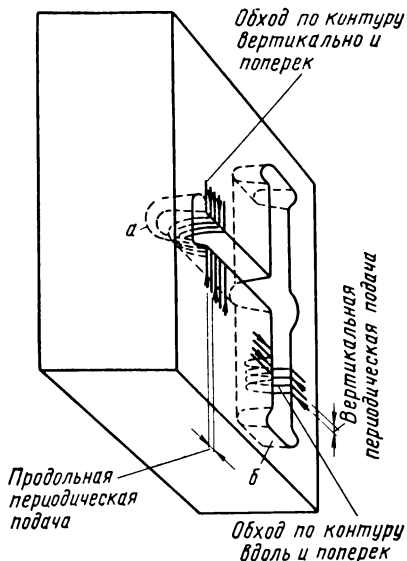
Два метода фрезерования трехмерных поверхностей, осуществляемые на станке 6441Б:
